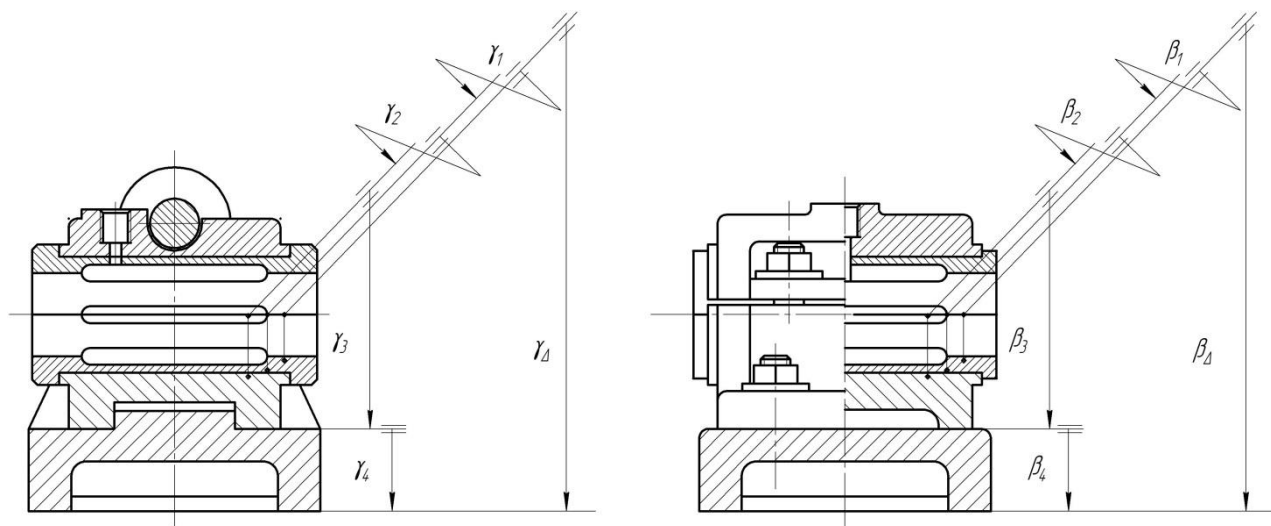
Розмірні ланцюги γ та β , які забезпечують точність розташування осей отворів вкладишів в рухомому корпусі та нерухомому корпусі
